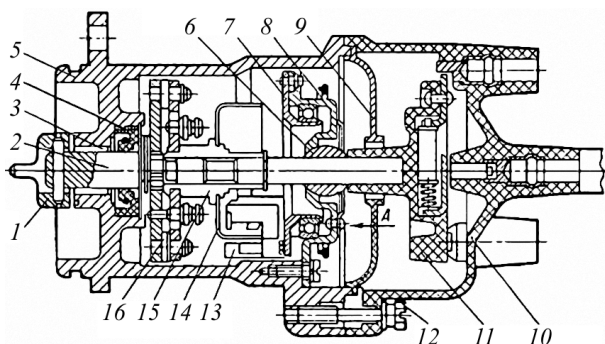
Датчик-распределитель: 1 – муфта; 2 – валик; 3 – втулка; 4 – манжета; 5 – корпус; 6 – шаровой вкладыш; 7 – подвижная пластина; 8 – неподвижная пластина; 9 – изоляционная прокладка; 10 – крышка; 11 – ротор; 12 – крепежный винт; 13 – датчик Холла; 14 – экран; 15 – втулка крепления экрана; 16 – центробежный регулятор
